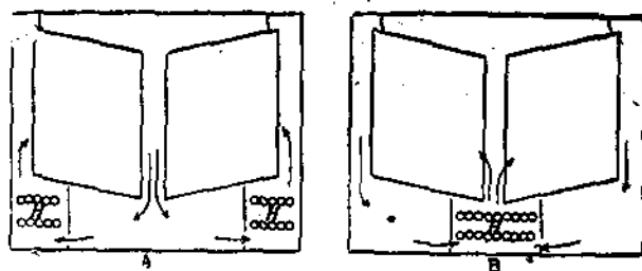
Схема сушила с наклонной штабелевкой и реверсивным движением воздуха
